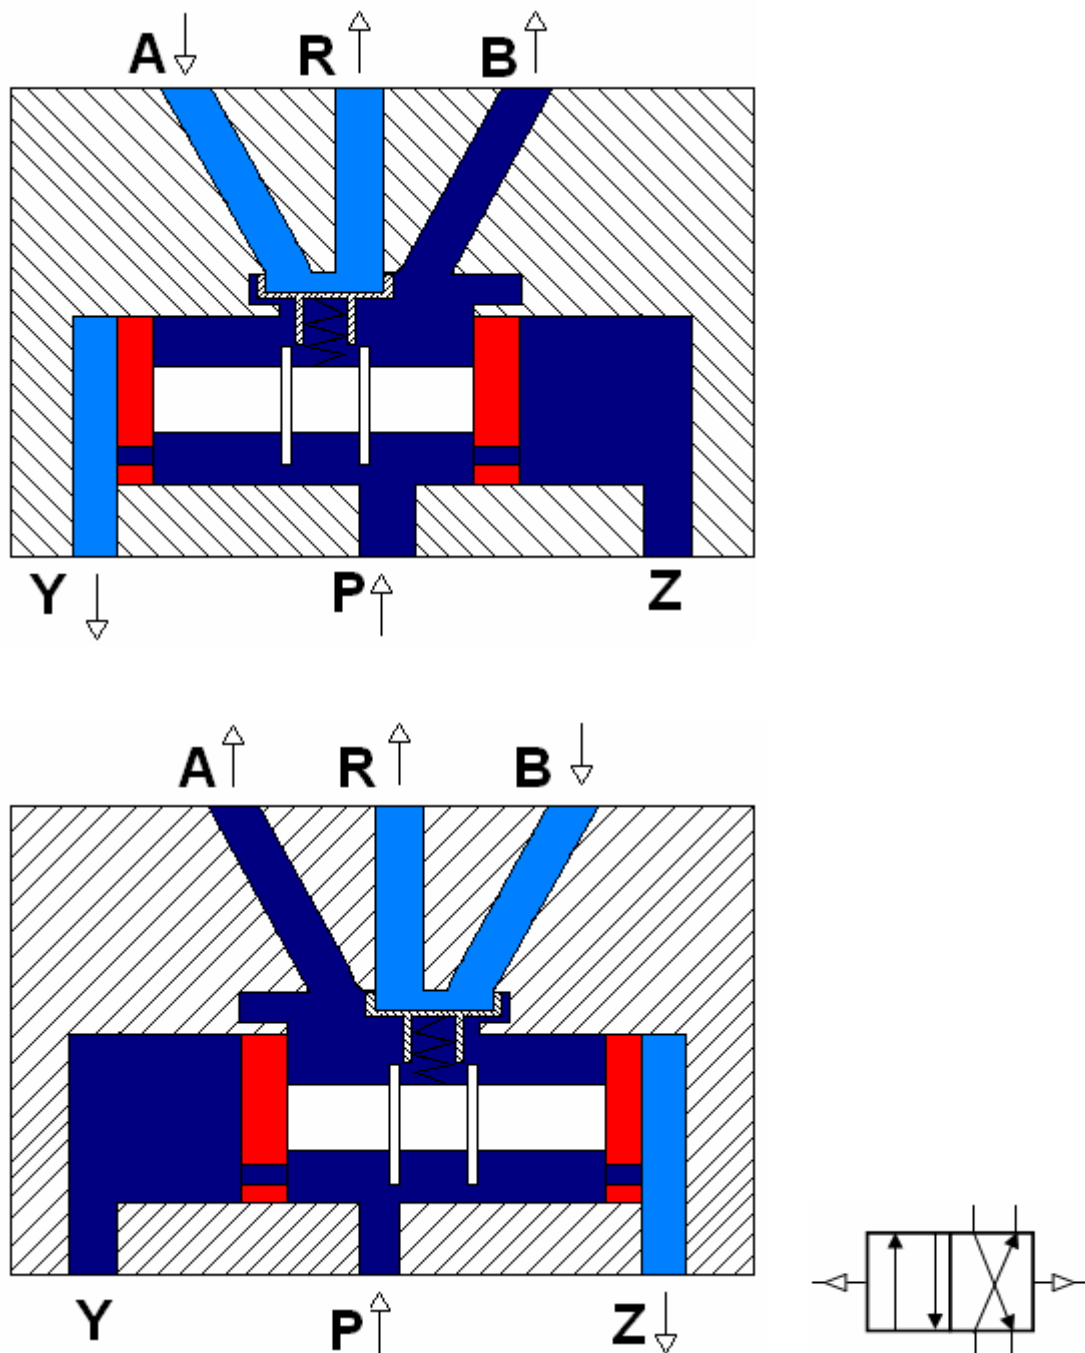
Rozvaděč 4/2 s plochým posuvným šoupátkem s pneumatickým ovládním dle [2]
